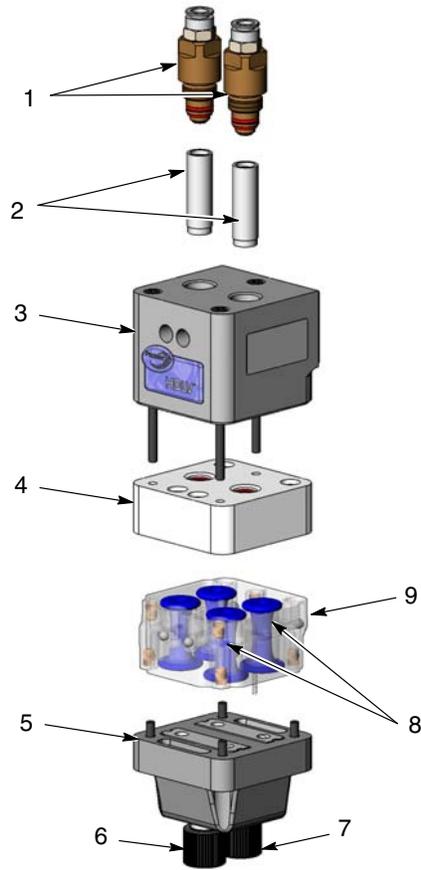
Componenti della pompa Prodigy HDLV
